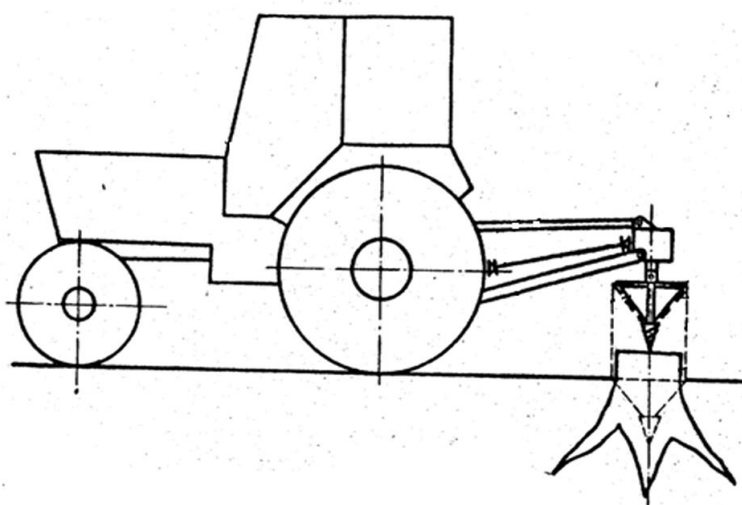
Схема ямокопателя-погрузчика ЯКП-0,4 (Украина) – сменное оборудование коническая фреза
